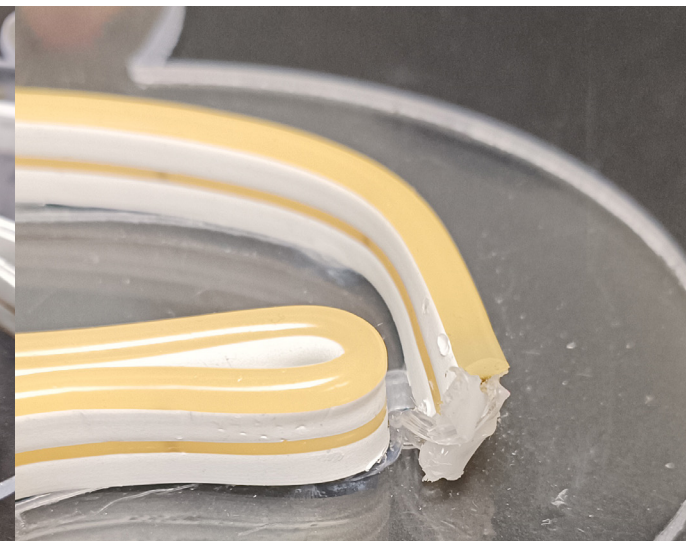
Si és necessari, fixar les soldadures amb una gota de silicona.
